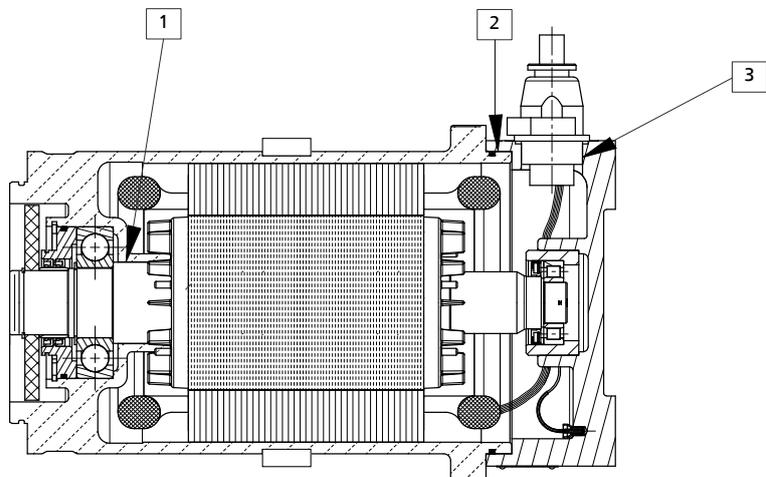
Ex-Spaltflächen bei explosionsgeschützten Motoren - Motortyp DKM161 / MA16
